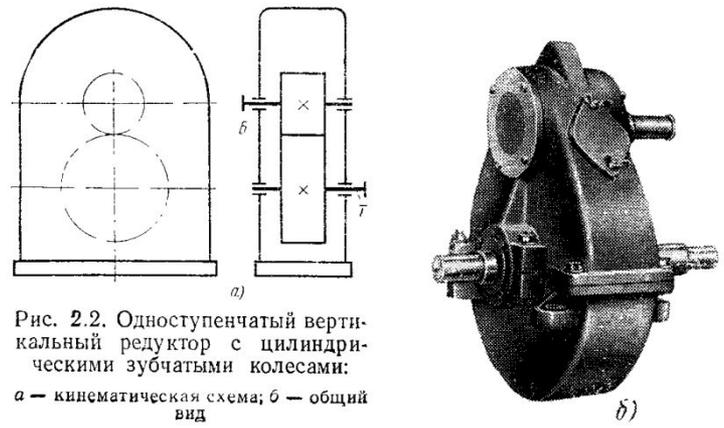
Одноступенчатый вертикальный редуктор с цилиндрическими зубчатыми колесами:
